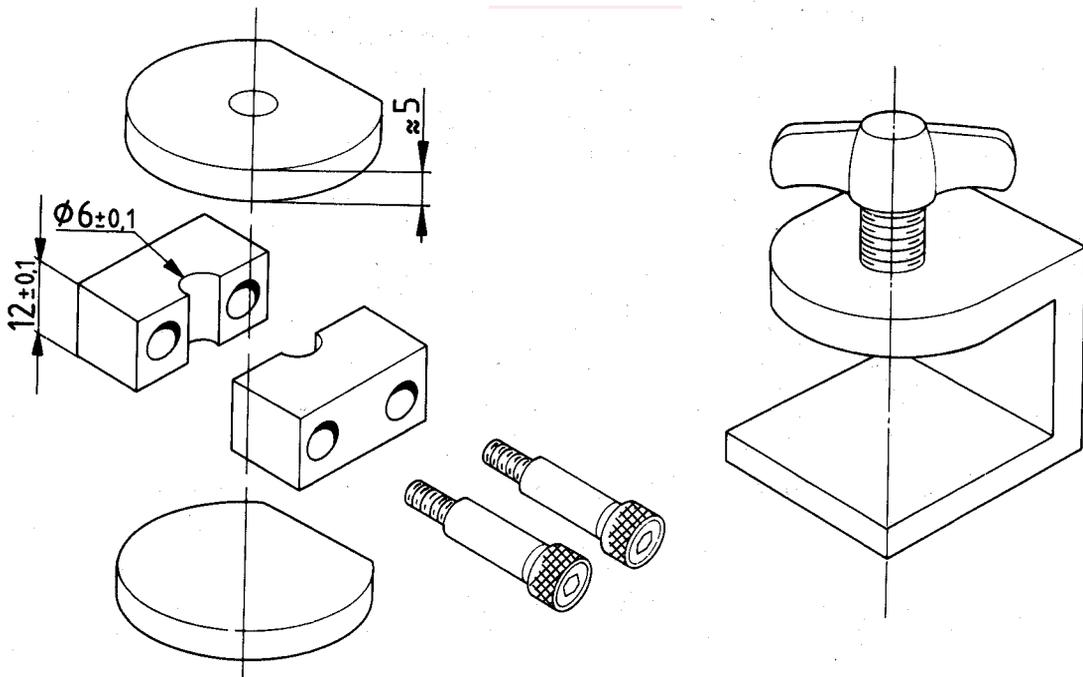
Moule et serre-joint pour la préparation des éprouvettes de résistance à la compression
